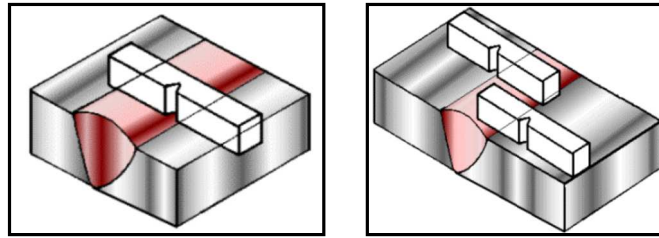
Localisation des éprouvettes dans un joint soudé.
